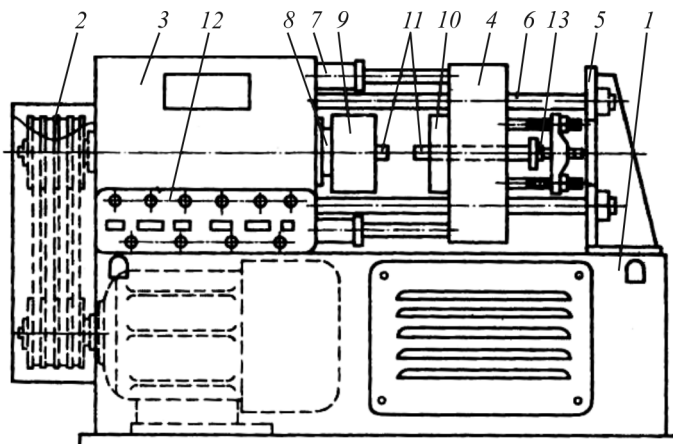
Принципиальная схема машины для СТ с непрерывным приводом: 1 – станина; 2 – привод шпинделя; 3 – передняя бабка; 4 – траверса; 5 – задняя стойка; 6 – направляющая штанга; 7 – гидравлические цилиндры осевого нагружения; 8 – шпиндель; 9 – зажимной патрон вращающейся заготовки; 10 – зажимное устройство неподвижной заготовки; 11 – свариваемые заготовки; 12 – пульт управления; 13 – упор для неподвижной заготовки
